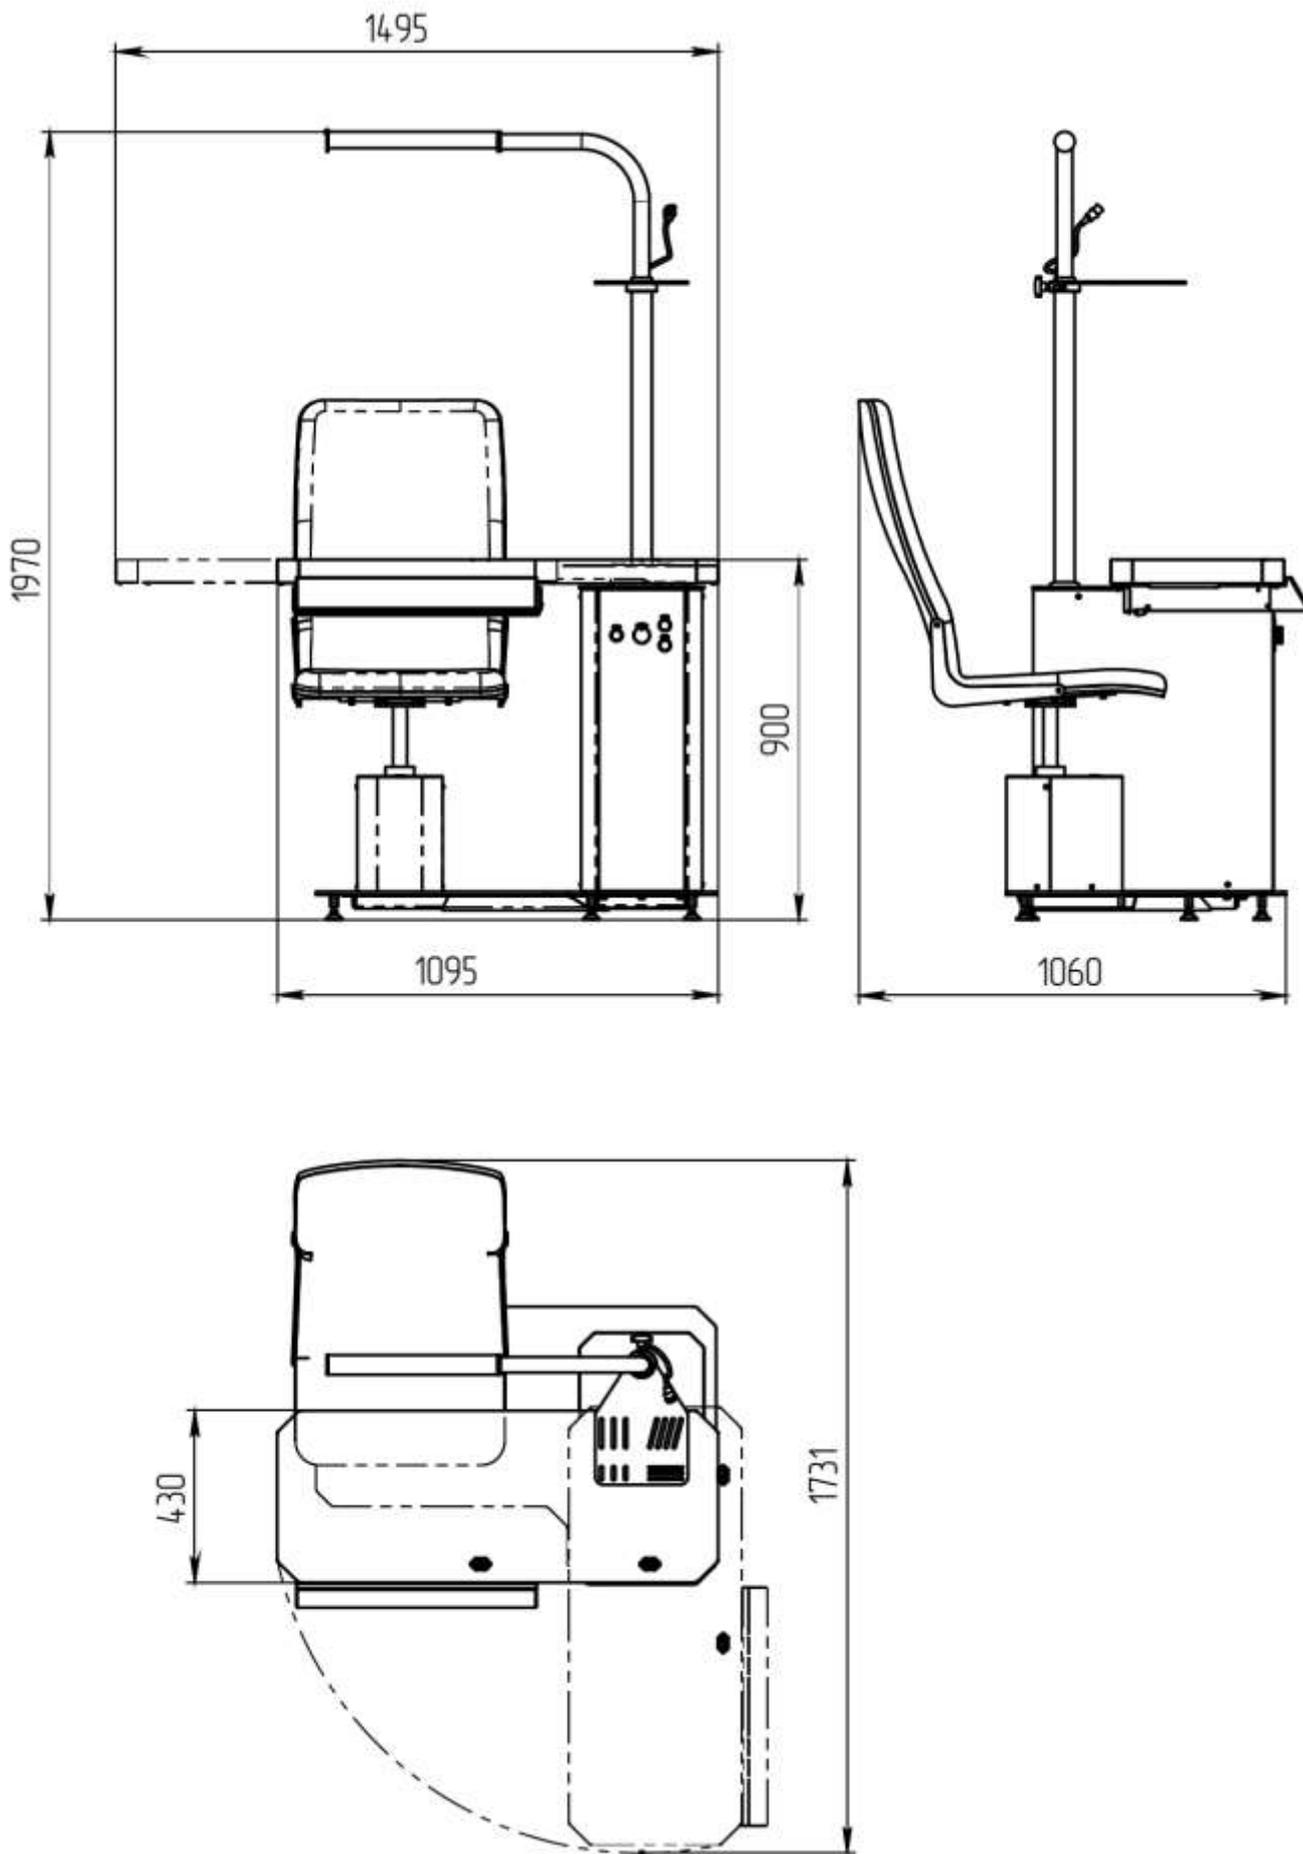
Виды и габаритные размеры Места рабочего: спереди, слева, сверху.
